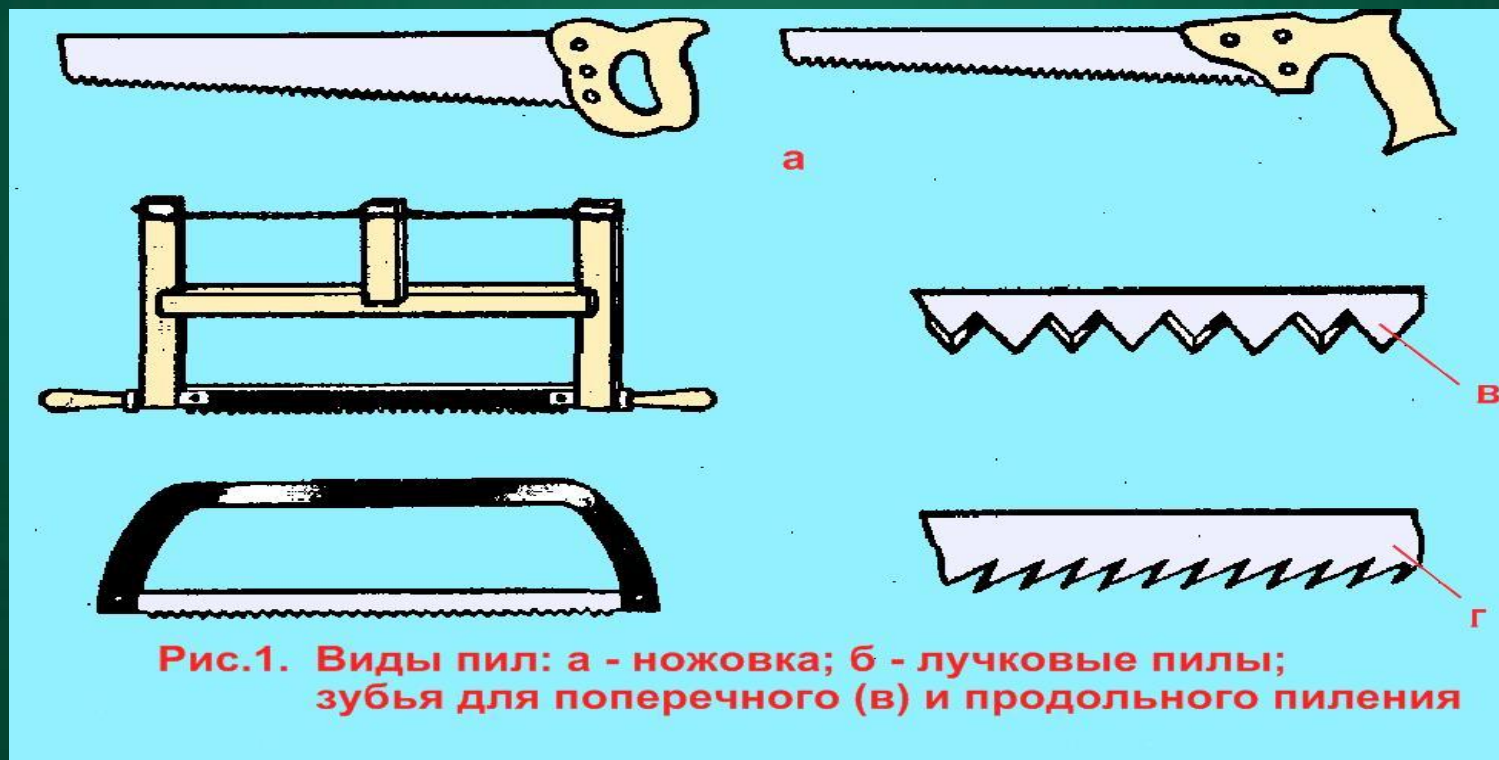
Виды пил: а - ножовка; б - луковые пилы; зубья для поперечного (в) и продольного пиления (г)
